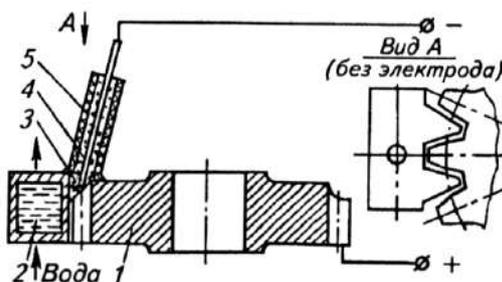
Схема наплавки торцов зубьев под флюсом:
